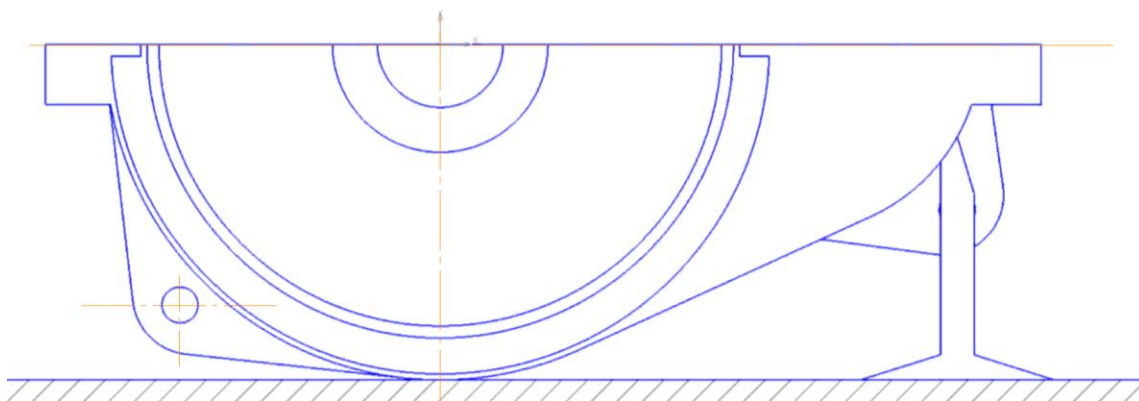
Нижняя часть корпуса редуктора - фронтальное изображение с подставкой
